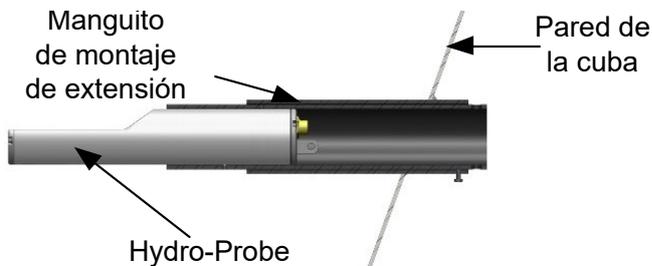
Hydro-Probe instalado en un manguito de montaje de extensión
